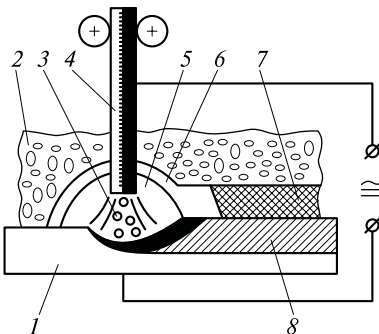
Схема дуговой сварки под флюсом:
